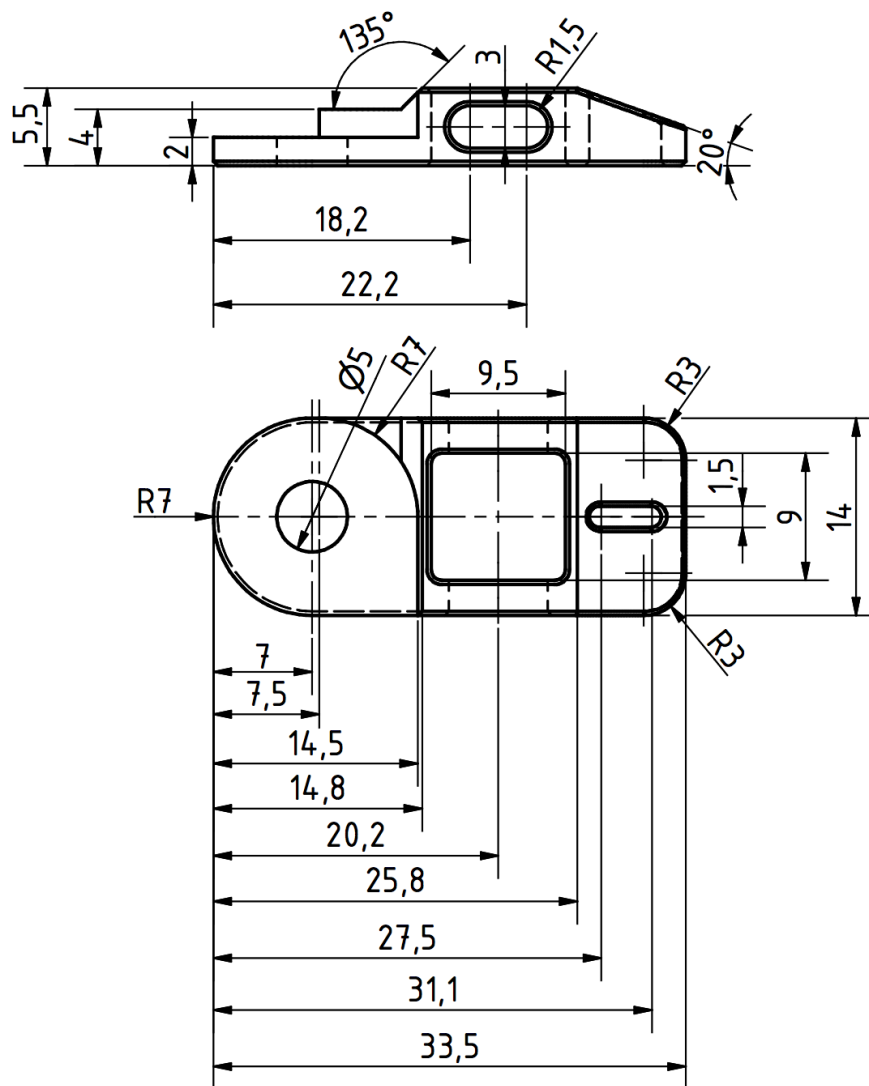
Technische Zeichnung proximaler Schenkel mit Maßen, Aufsicht und Seitansicht.
